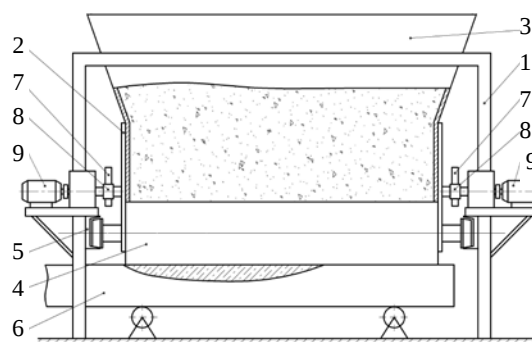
Роликовая формовочная установка с кулачковым приводным механизмом
